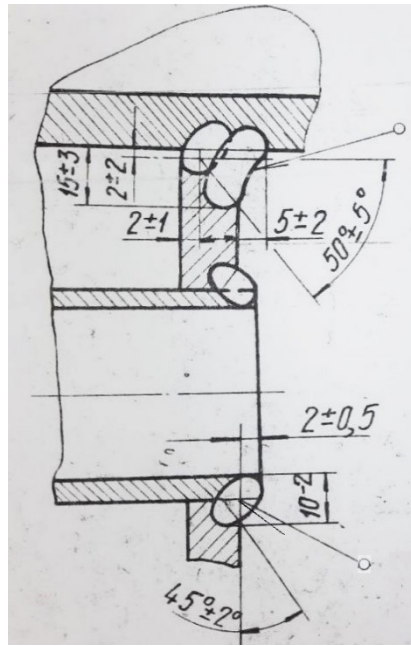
Сварное соединение трубы с трубной решеткой в котлах типа КАВ
